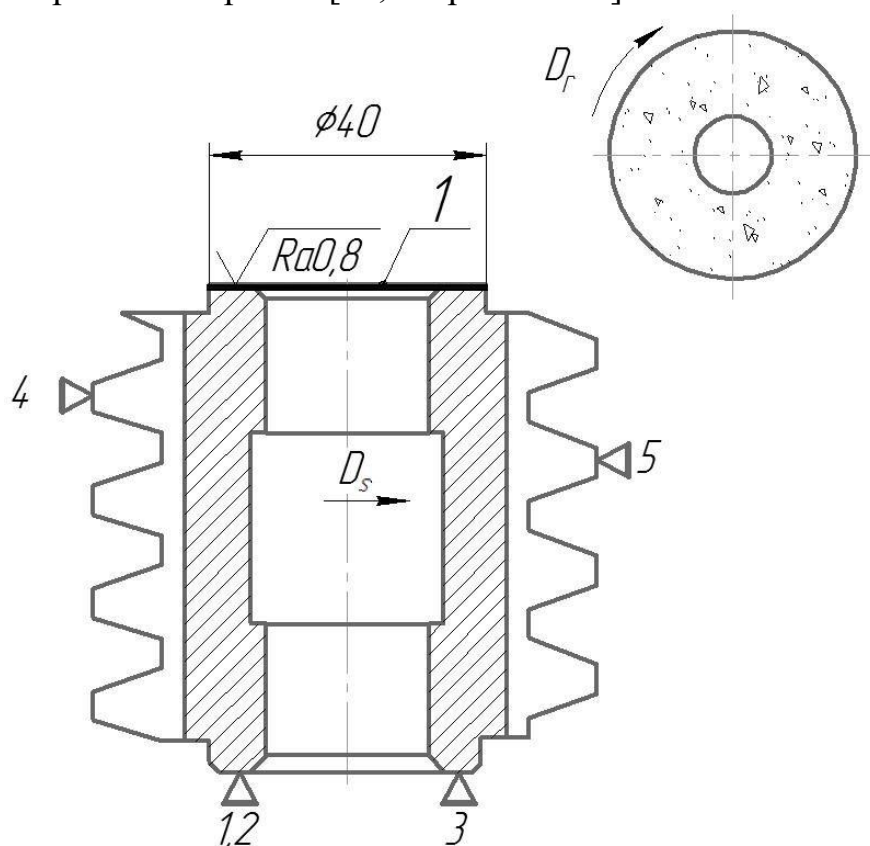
Ескіз абразивної обробки торцевої поверхні фрези
